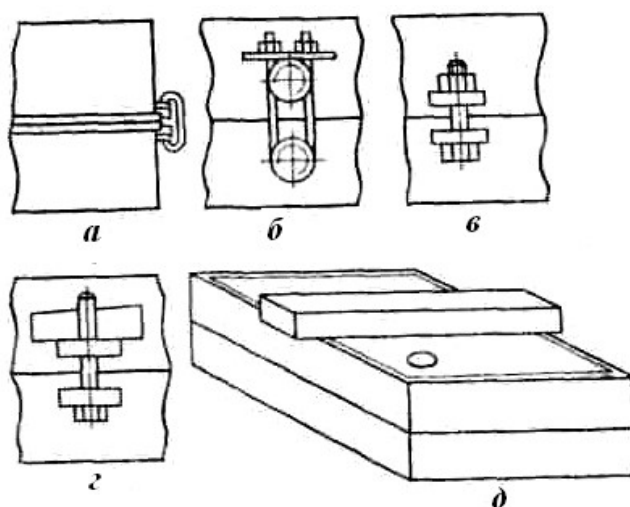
Способы крепления полуформ: а — сковами; б — струбцинами; в — болтами; г — клиньями; д — установкой груза
